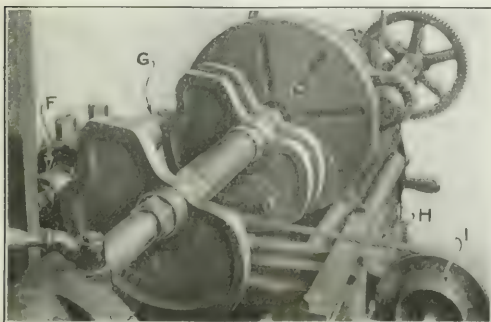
TORNO ACONDICIONADO PARA FRESAR EXCÉNTRICOS
